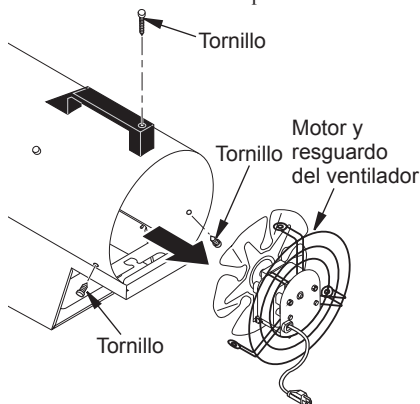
Desmontaje del motor y el resguardo del ventilador del calentador
